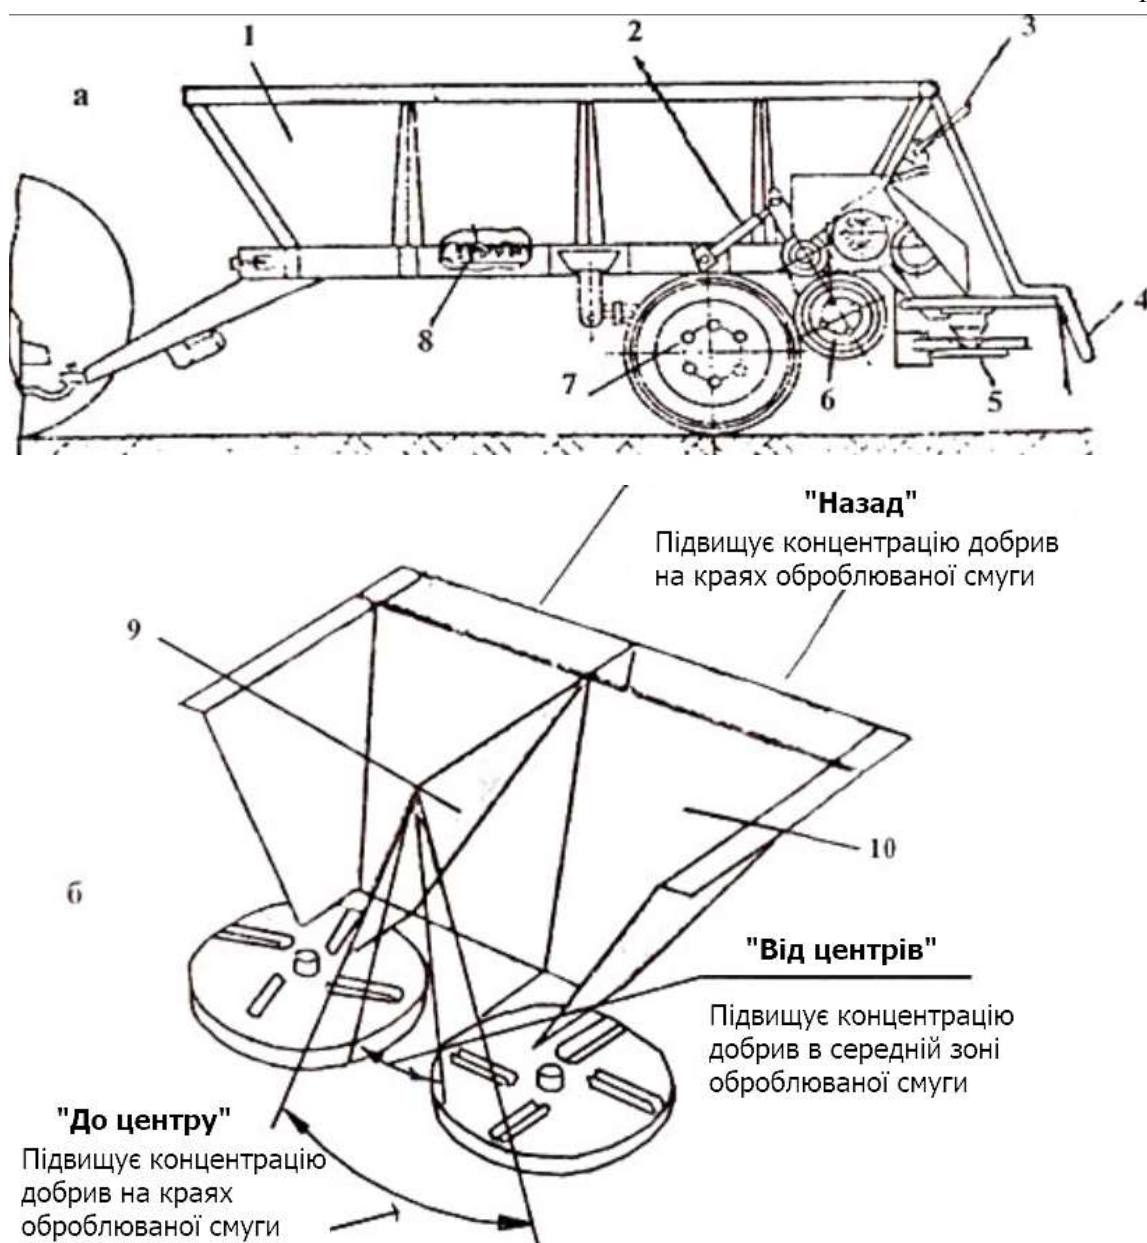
Розкидач мінеральних добрив 1-РМГ-4: а - схема роботи; б - схема тукоподільника; 1 - кузов; 2 - гідроциліндр; 3 – дозувальний пристрій; 4 - вітрозахисний пристрій; 5 - диски; 6 - ролик; 7 - ходове колесо; 8 - транспортер; 9 - шарнірна стінка; 10 - тукоподільник.
